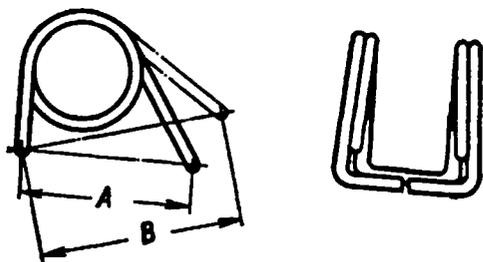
Схема проверки пружины рычага: А - размер в свободном состоянии; В - размер под нагрузкой
